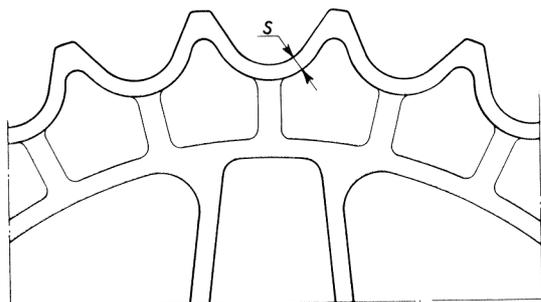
Epaisseur (s) du cordon latéral des dents de barbotin.
